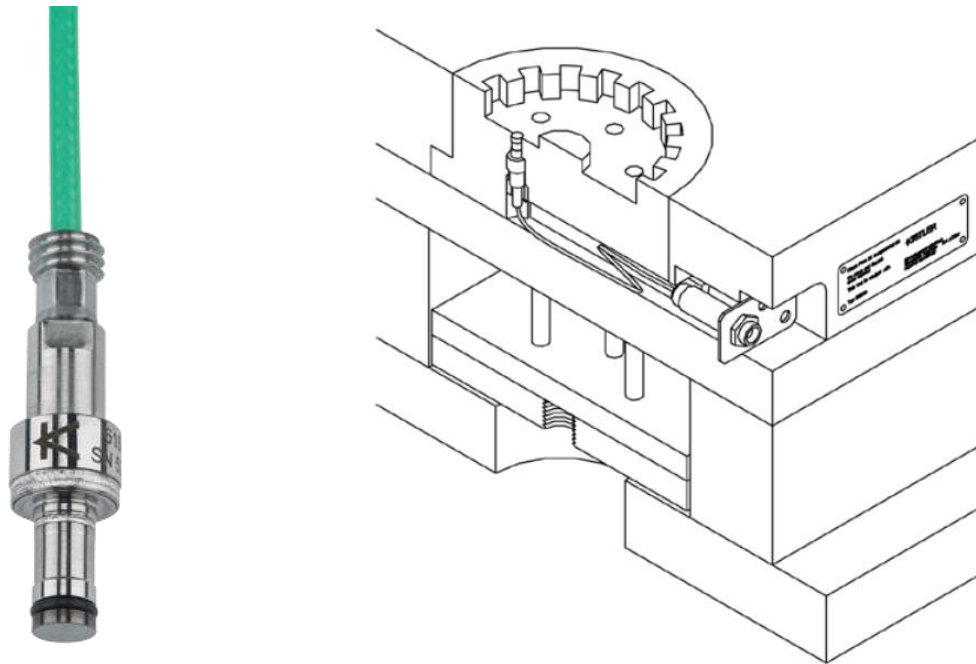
Direktmessender Werkzeuginnendrucksensor (links, [7]) und dessen beispielhafter Einbau in ein Spritzgießwerkzeug (rechts, [8])
